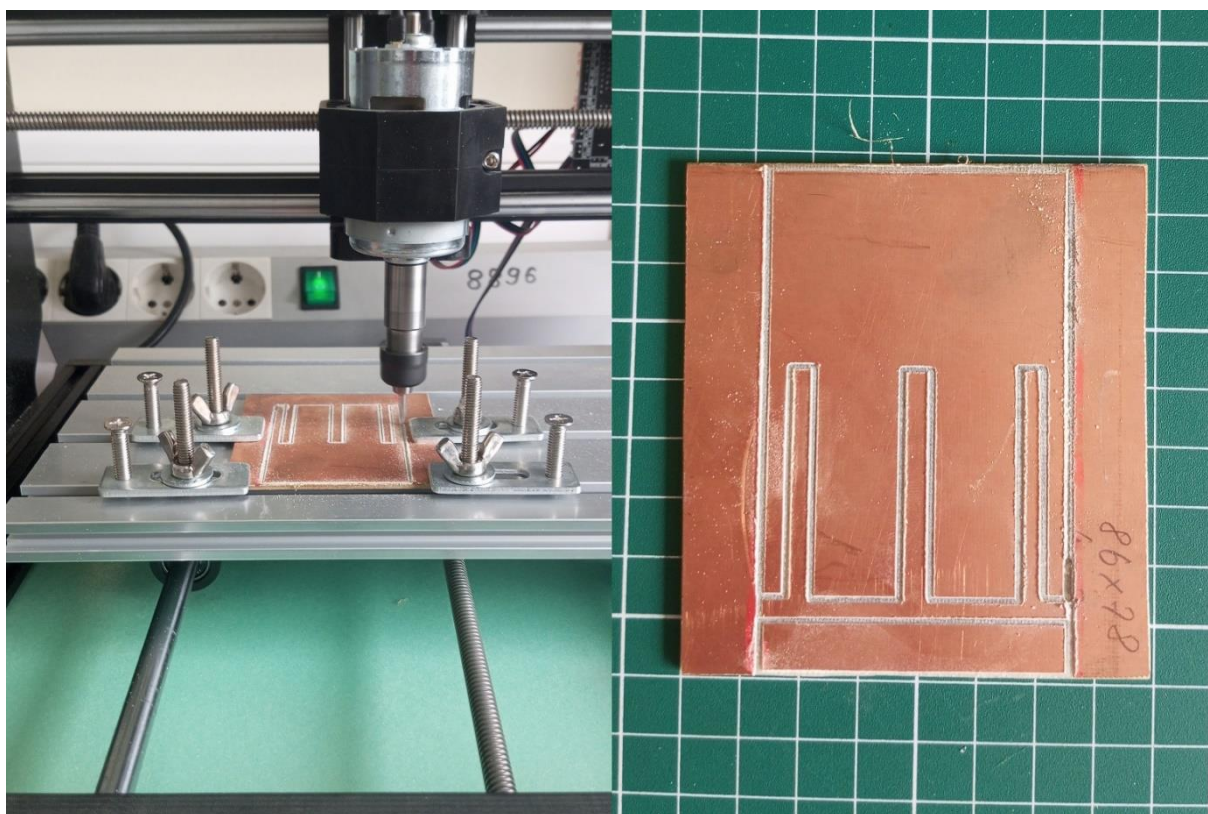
Изготовление ППФ на фрезерном станке с ЧПУ
